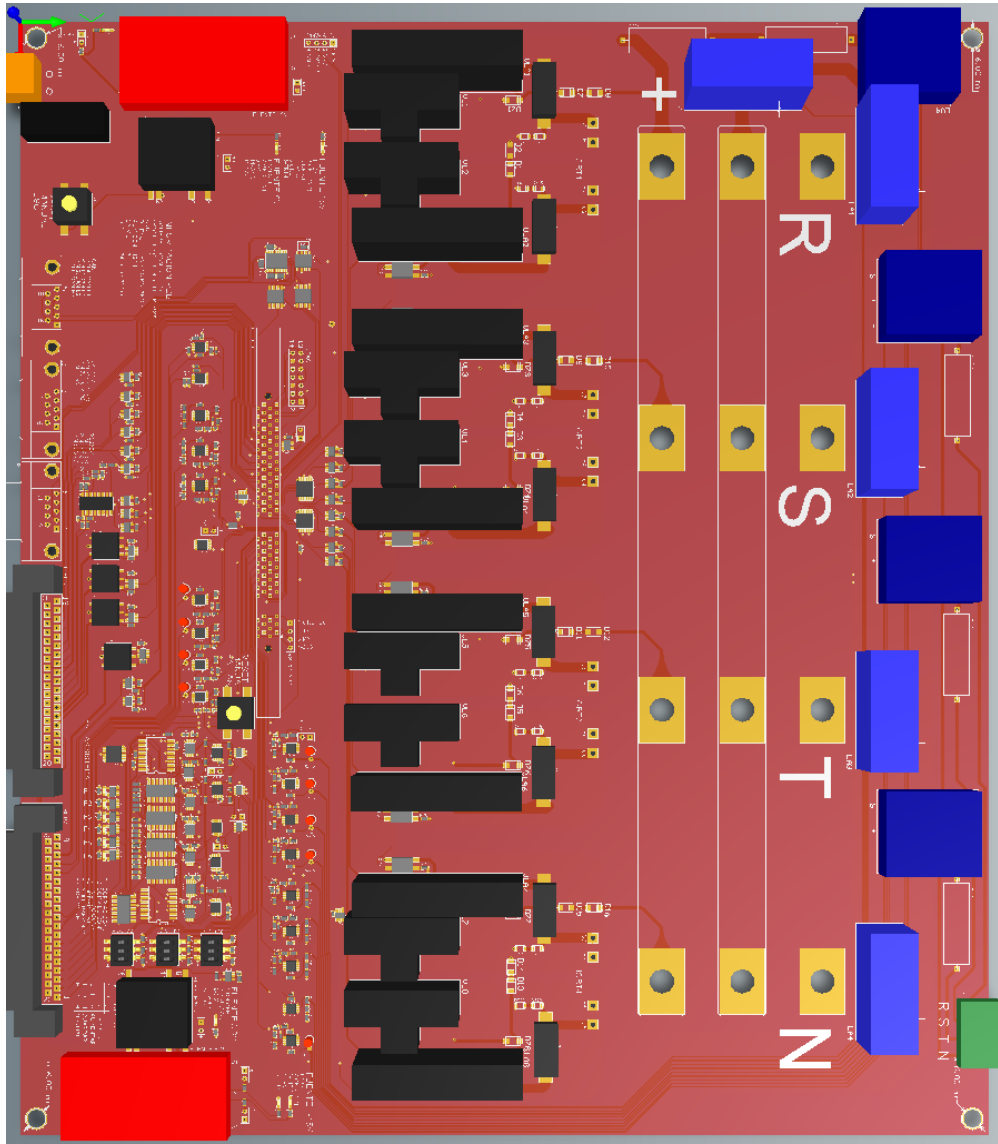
Vista superior diseño PCB Controlador de Potencia
